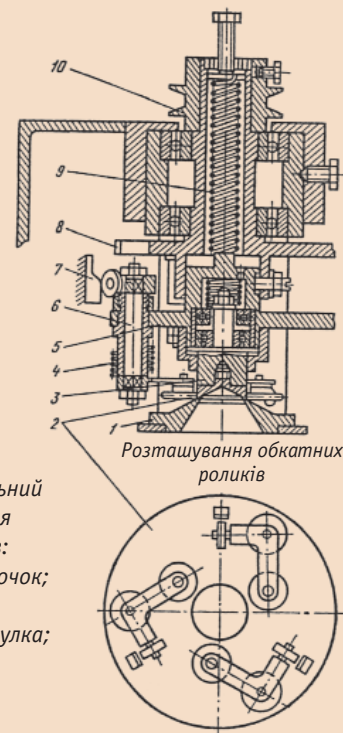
Закупорювальний обкатний механізм для алюмінієвих ковпачків:
